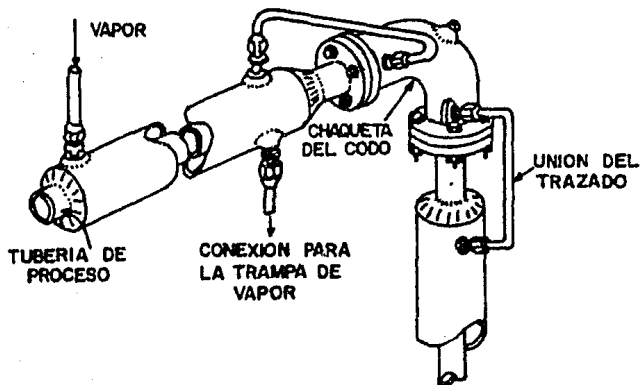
ENCHAQUETADO DE UNA TUBERIA DE PROCESO Y UN CODO.
